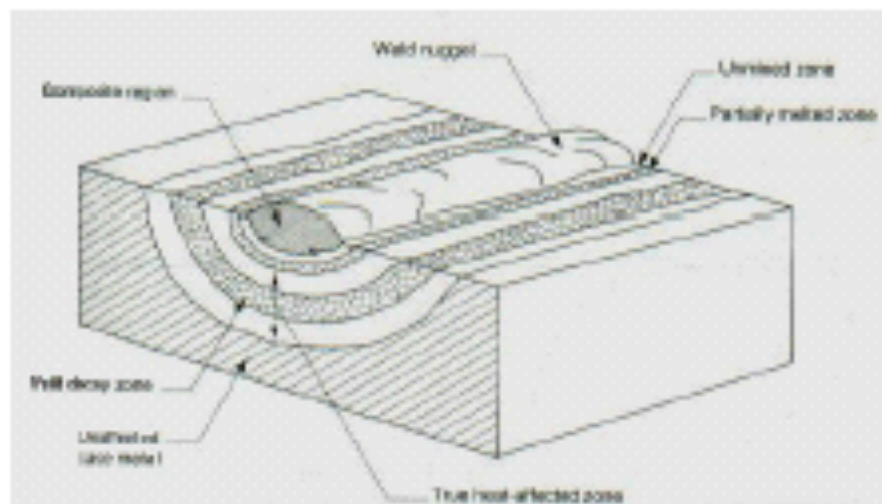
Esquema de la Microestructura de una Soldadura. Principles and Prevention of Corrosion. Denny A. Jones. 1992. Pág. 309.
